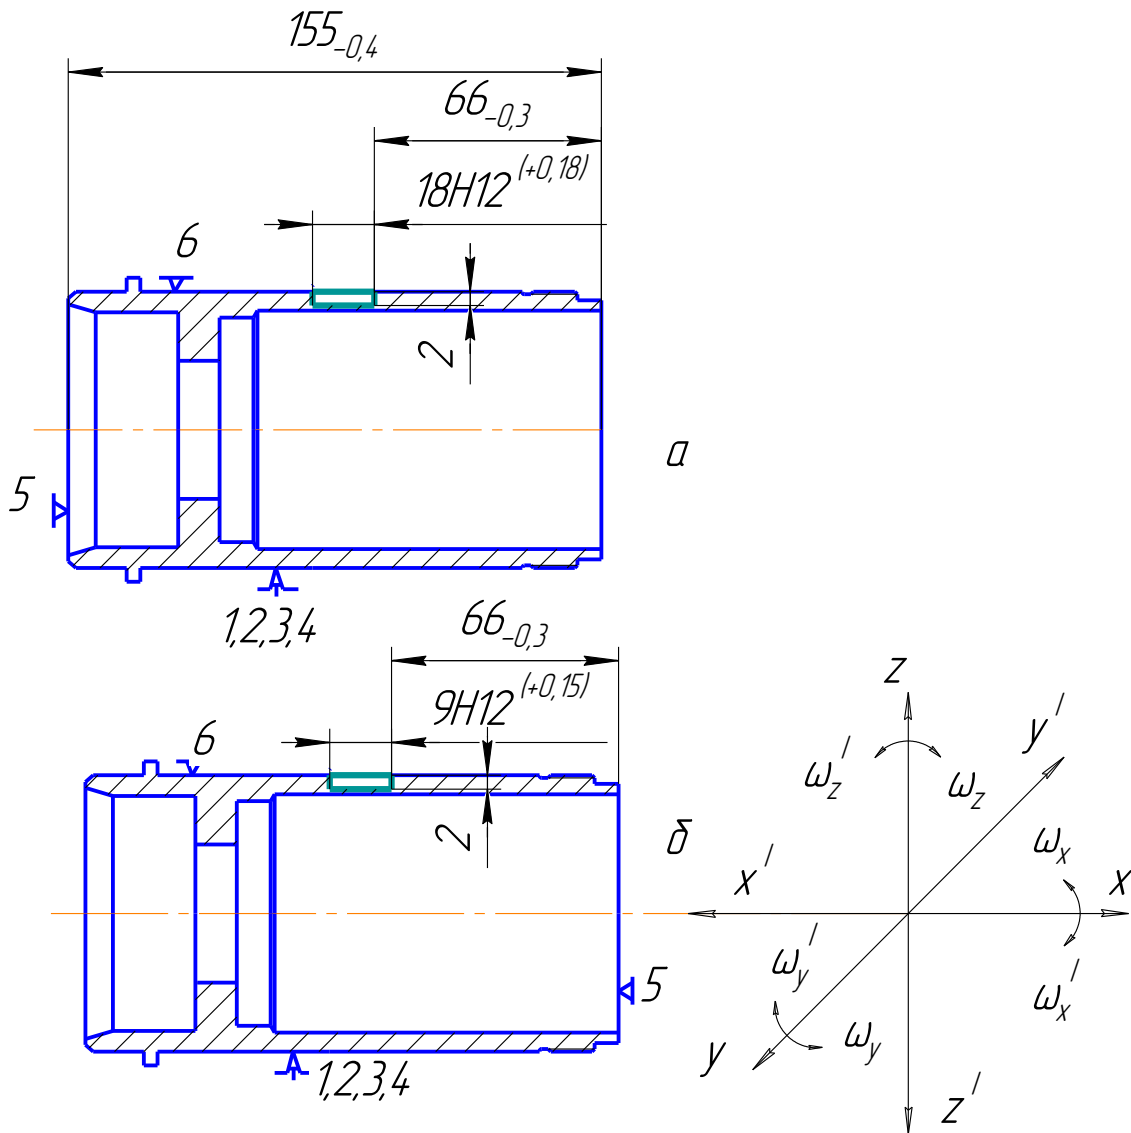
Варіанти базування: а - перший варіант;
